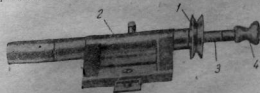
Простой фрезерный супорт (вертикальный) супорт.
